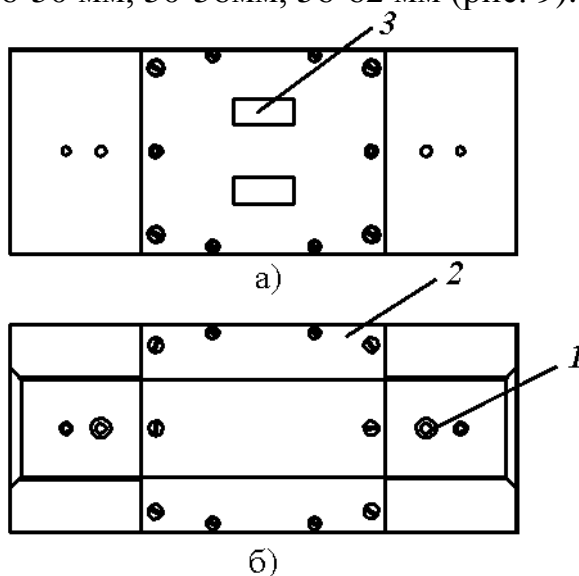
Съемные полюса: (а - вид сверху, со стороны движения каната; б - вид снизу, со стороны крепления к основным полюсам): 1 - отверстия для крепления съемного полюса; 2 - немагнитная арматура полюса; 3 - контакты разъема для подключения датчиков к измерительным преобразователям.
